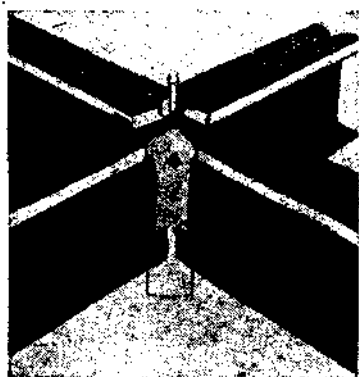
Крестовина в собранном для сварки виде.
